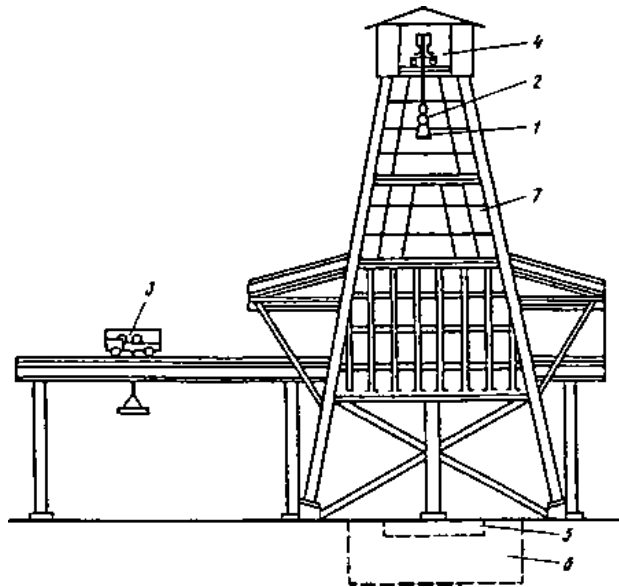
Баштовий копер для подрібнення металевго брухту:
